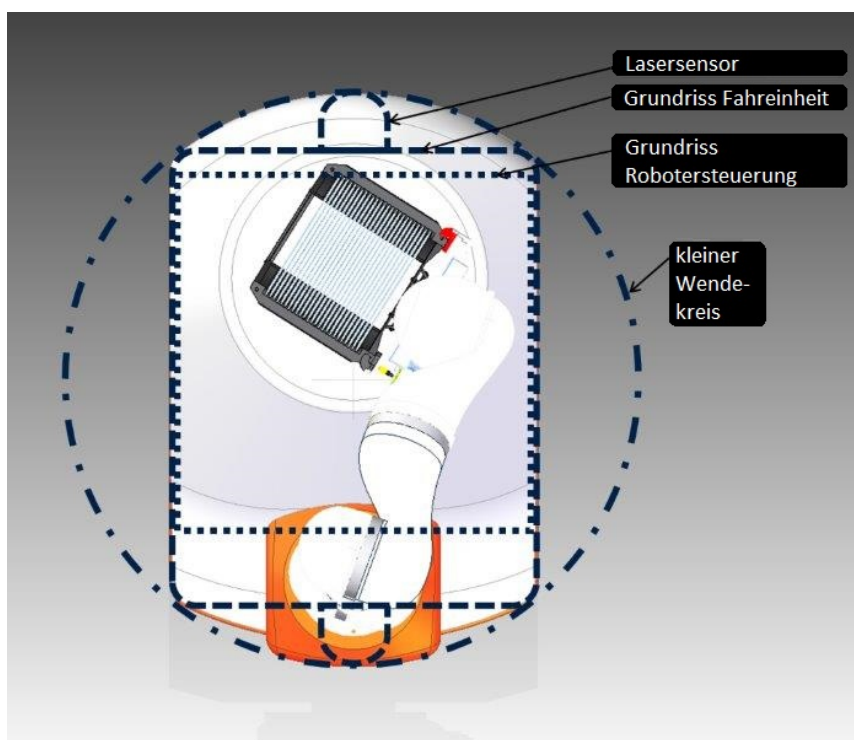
Designvorschlag Grundriss.
